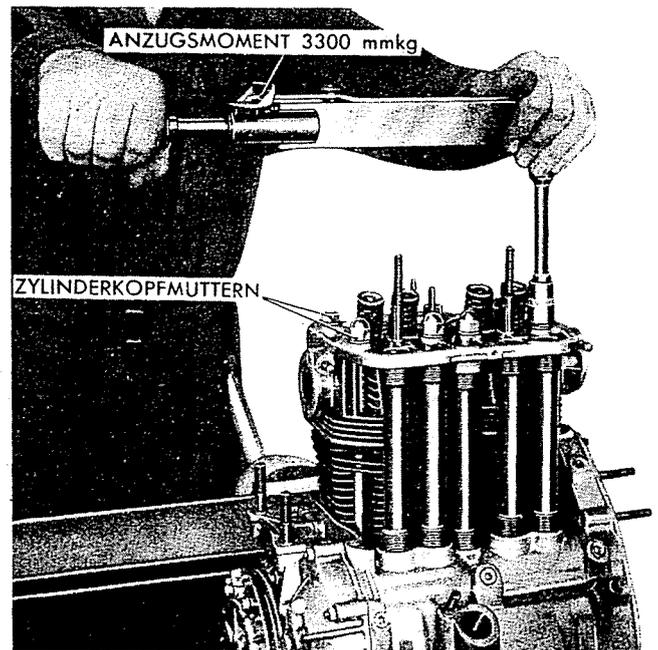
Anziehen der Zylinderkopfmutter mit dem Drehmomentschlüssel.
